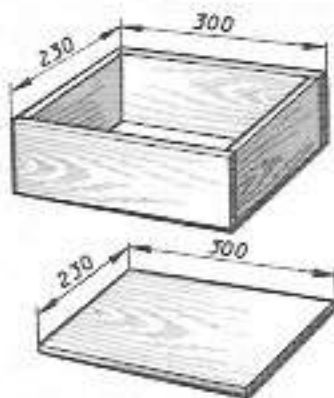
Боковые стенки ящика и заготовка для дна.
